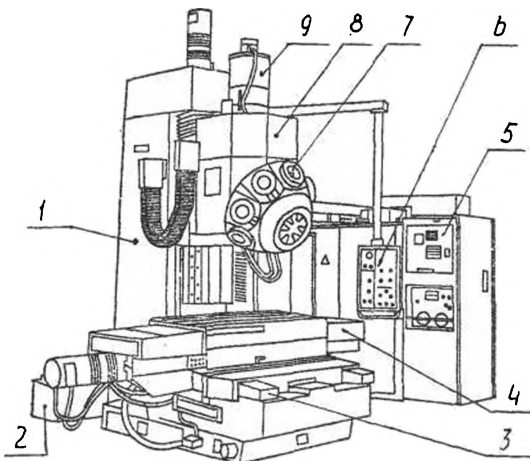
Загальний вигляд вертикально-фрезерного верстата моделі ЛФ260МФЗ
